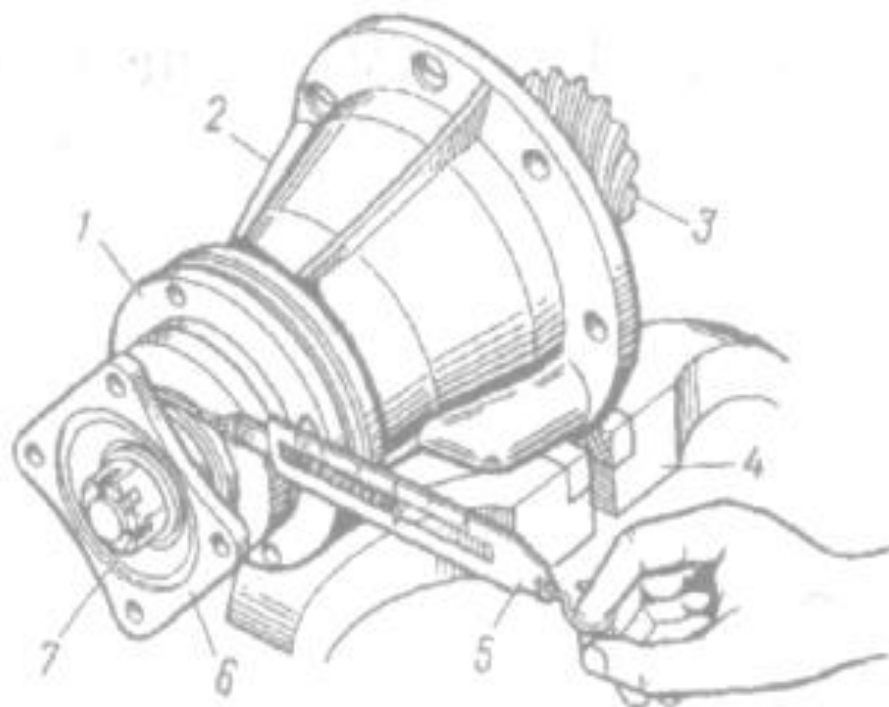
Проверка затяжки подшипников вала ведущей шестерни
